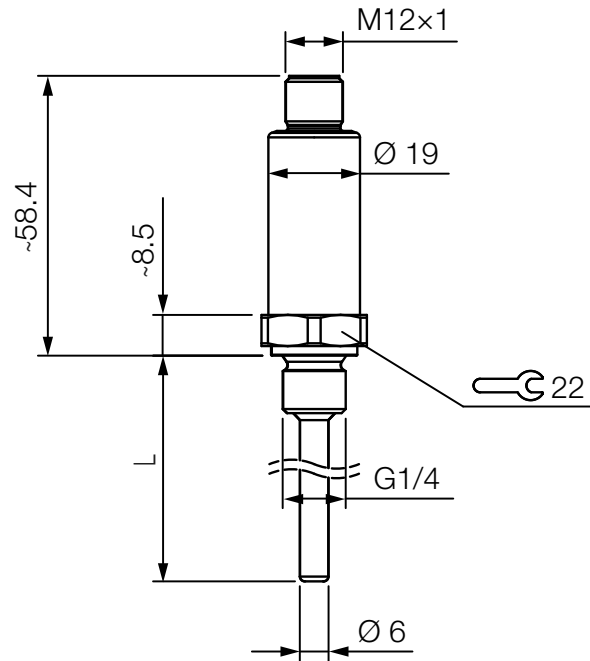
Prozessanschluss mit zylindrischem Gewinde
